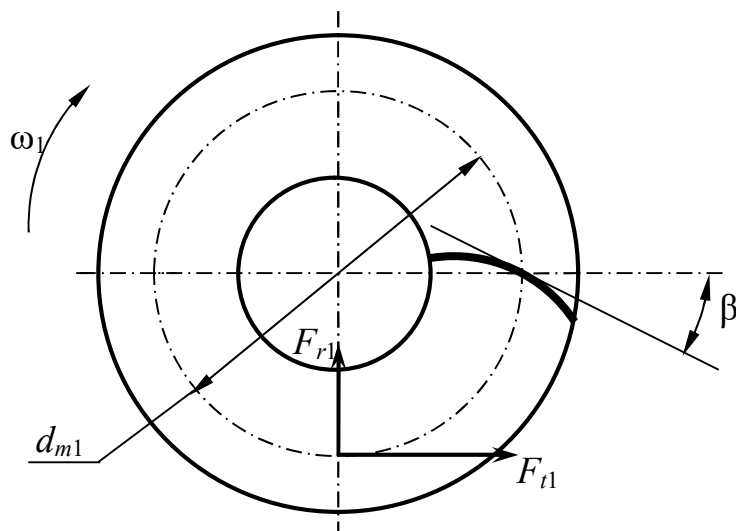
Коническая шестерня с круговым зубом (вид со стороны вершины конуса)
